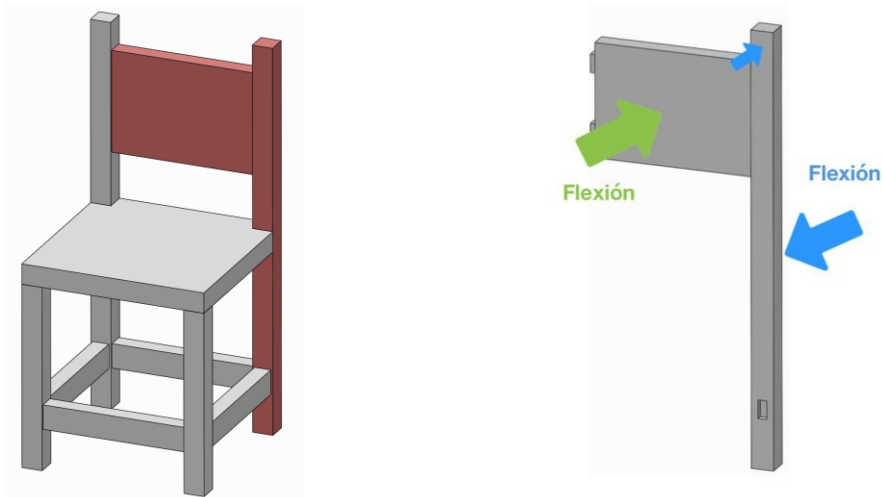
Esfuerzos unión plancha + horizontal || Fuente: Elaboración propia
